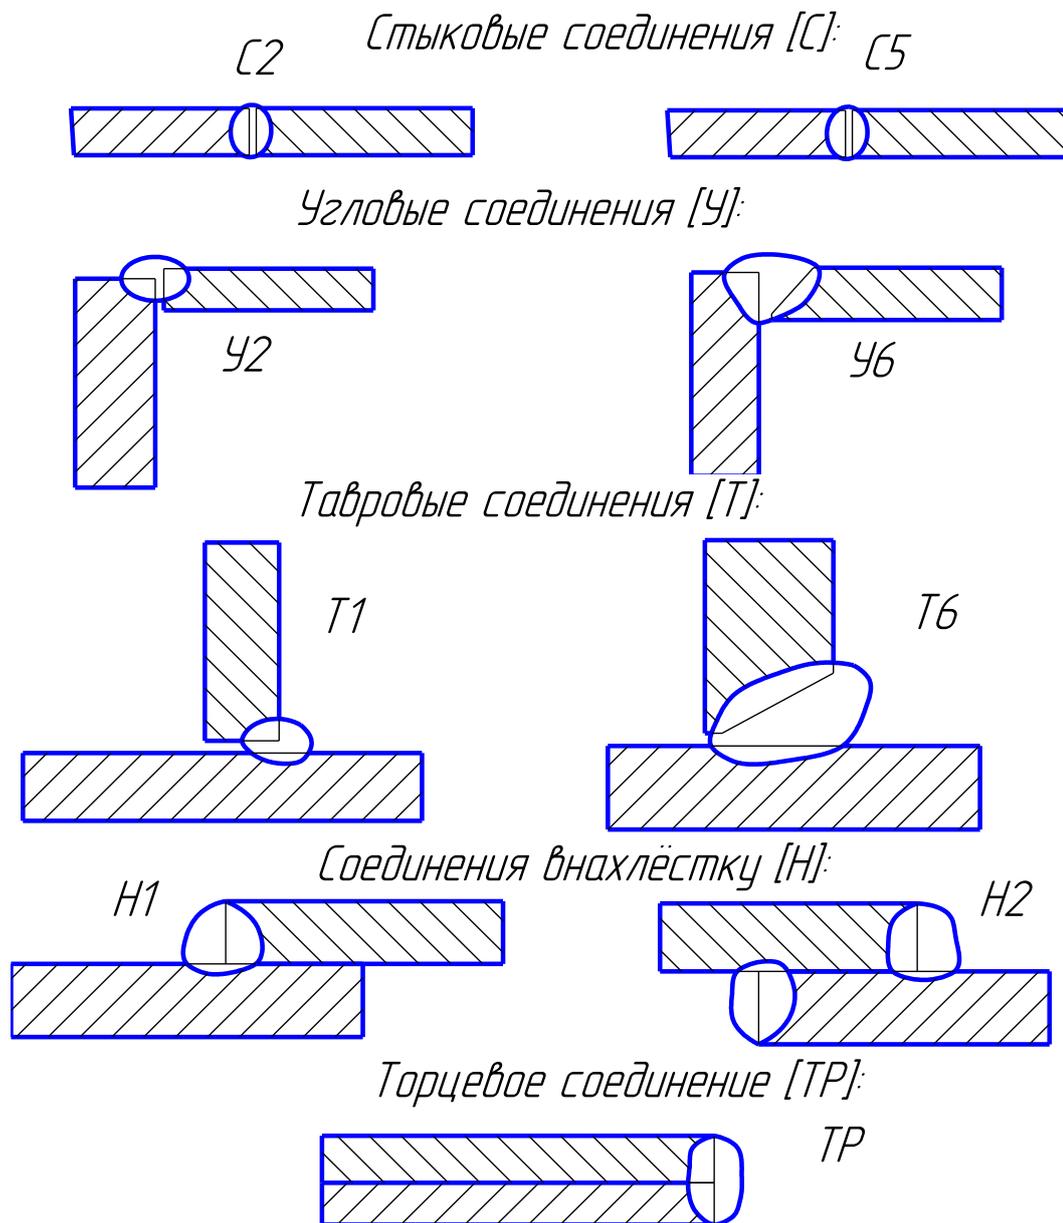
Примеры типов и буквенно-цифровых обозначений сварных швов
